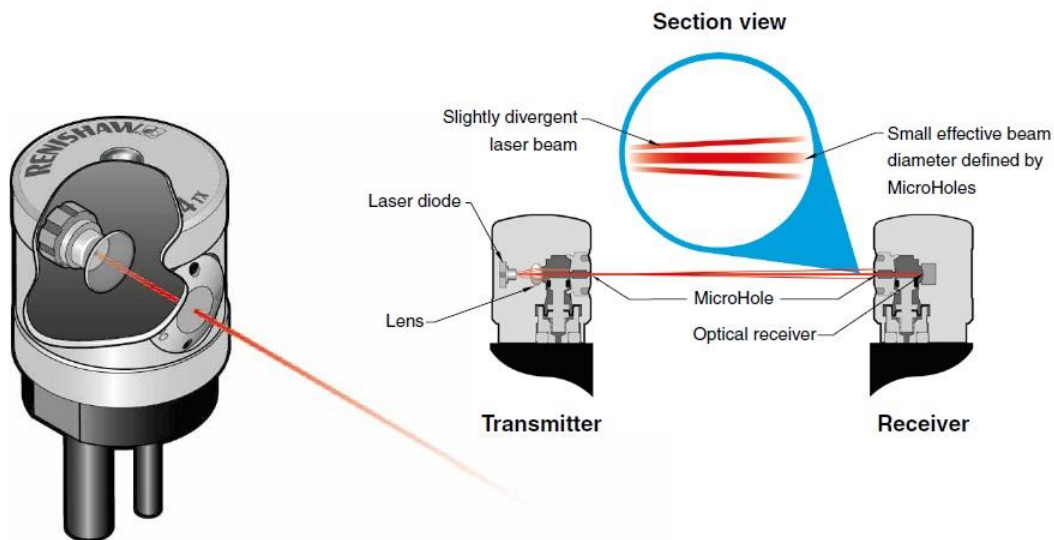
Princípio de funcionamento de um sistema laser para medir ferramentas (Renishaw, Probing Systems for CNC Machine Tools, 2014)
